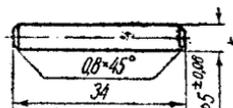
Дет. № 3257. Штифт цилиндрический к шестерне спиральной
